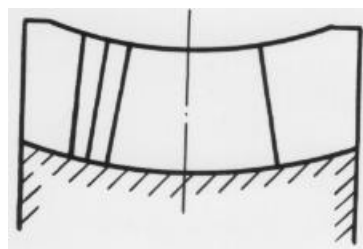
Розташування контактних ліній на поверхні зуба колеса.
